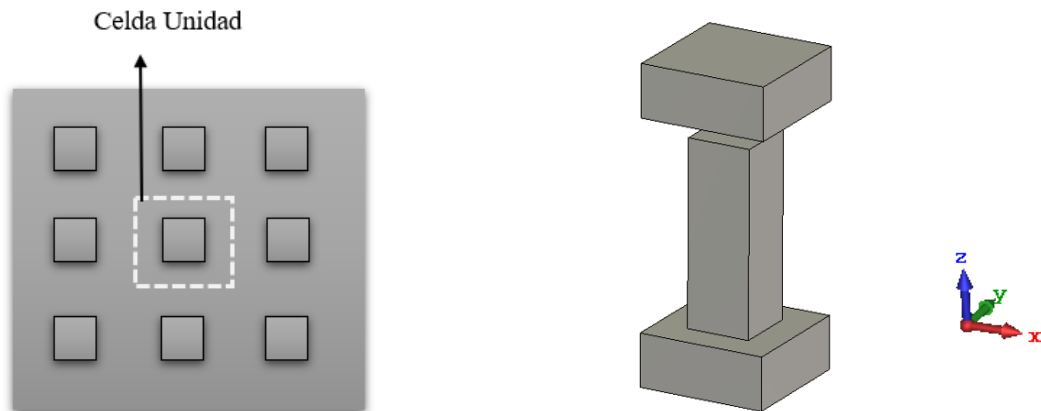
a) Conjunto pines 3x3. b) Diseño celda pin
